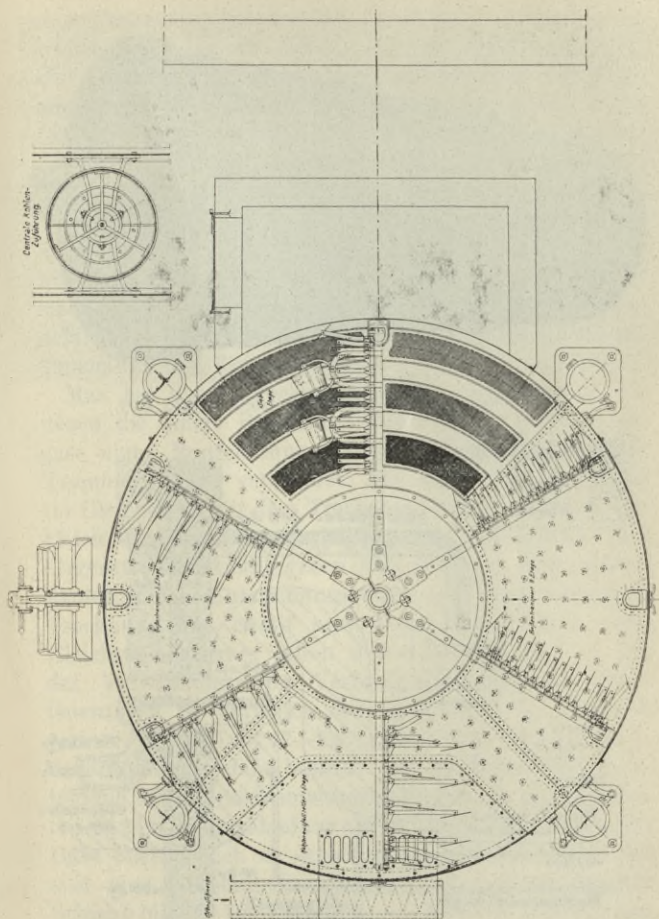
c. Teller Trockner, Grundriß. Ausführung der Maschinenfabrik Buckau A.-G.
